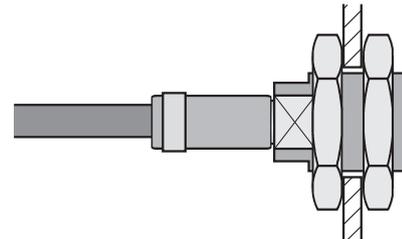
Geschirmter Sensor mit Gewinde in Standardmontage
